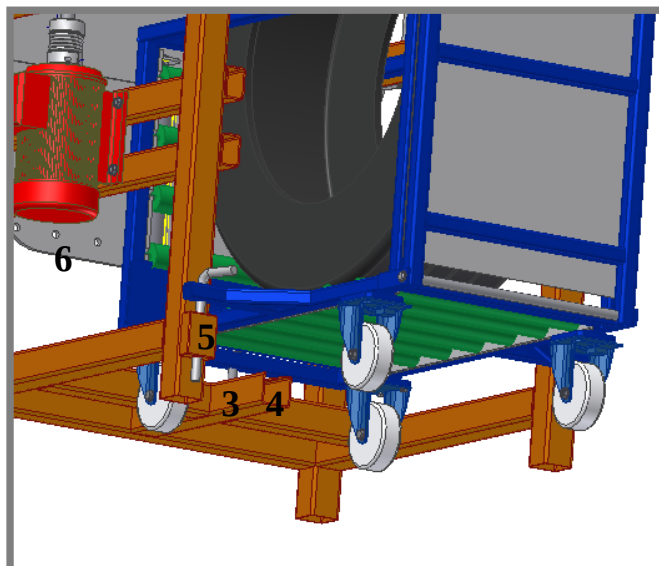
Vozík s otevřenou výklopnou konstrukcí
